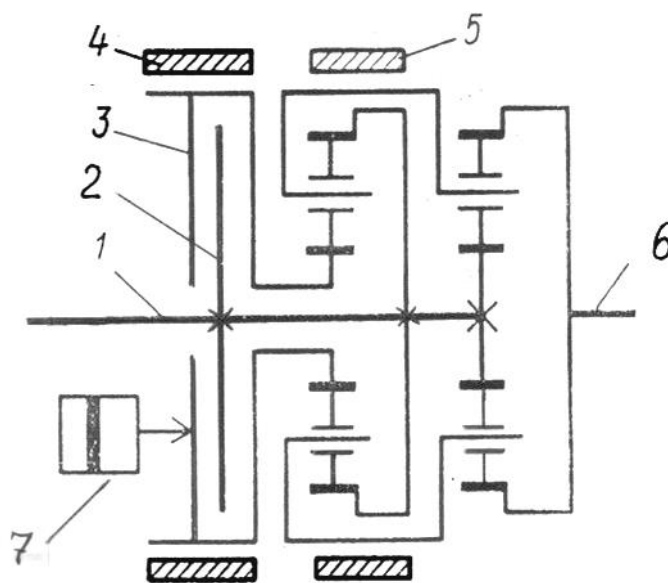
Схема двухступенчатой планетарной коробки передач:
